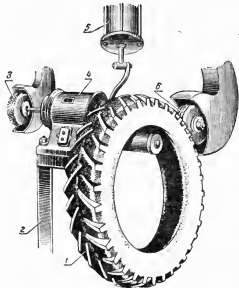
Наружная (местная) шероховка покрышки на шероховальном станке:
